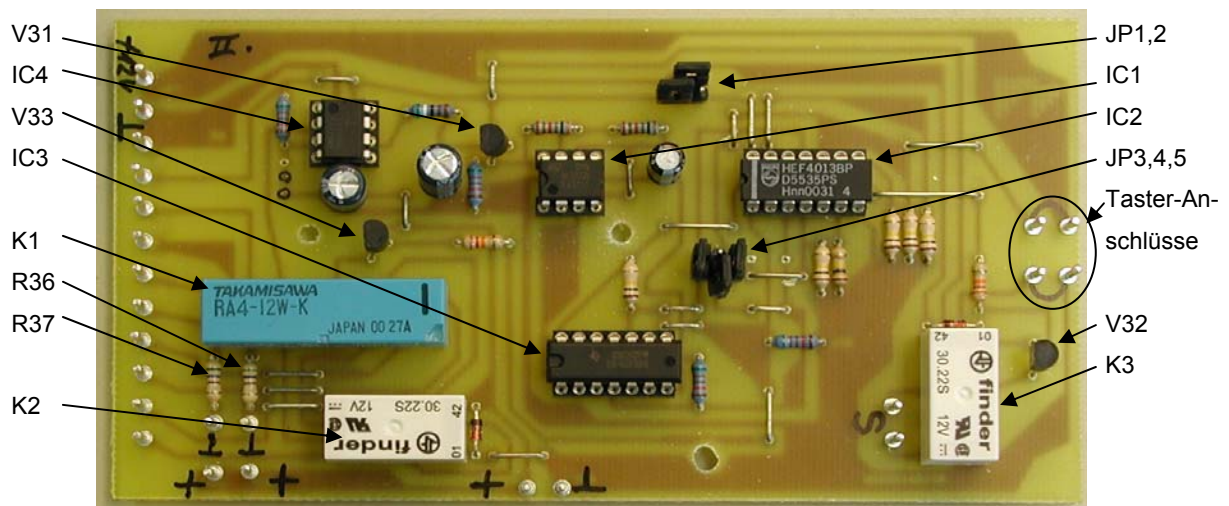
Hauptplatine für das EC-Steuergerät. Wichtige elektronische Bauteile sind bezeichnet.
